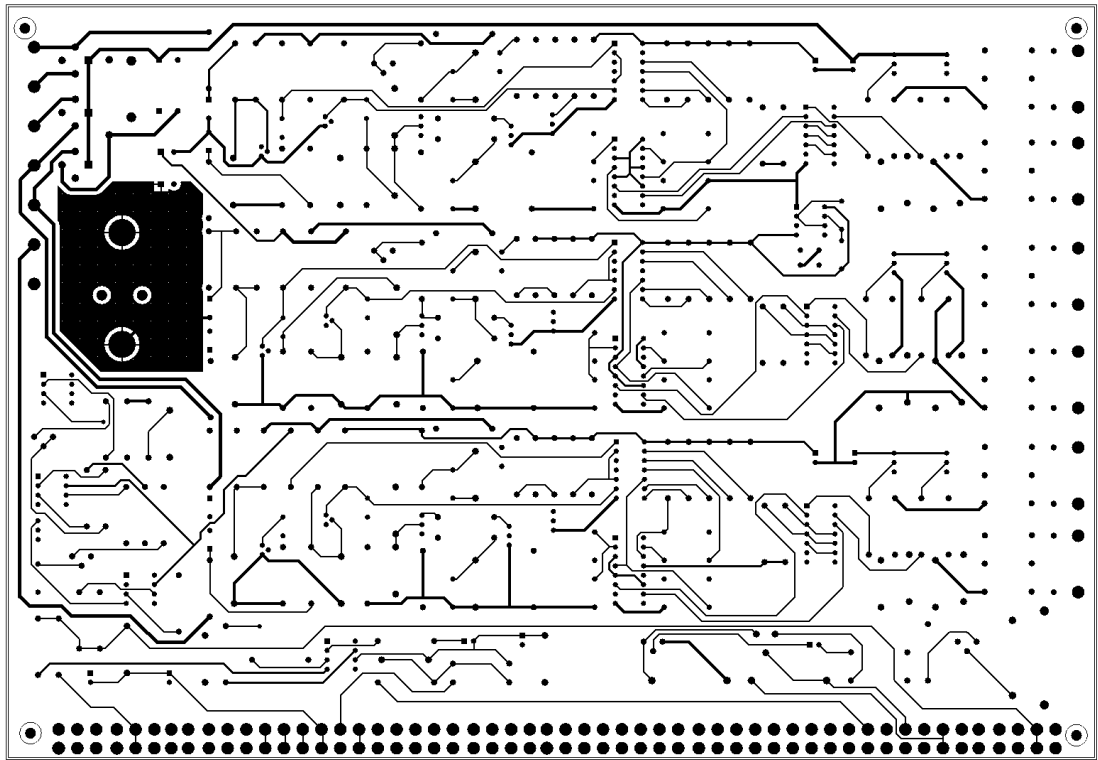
DISEÑO PCB DE TARJETA DC 2554 DE REEMPLAZO (REDUCCIÓN)
